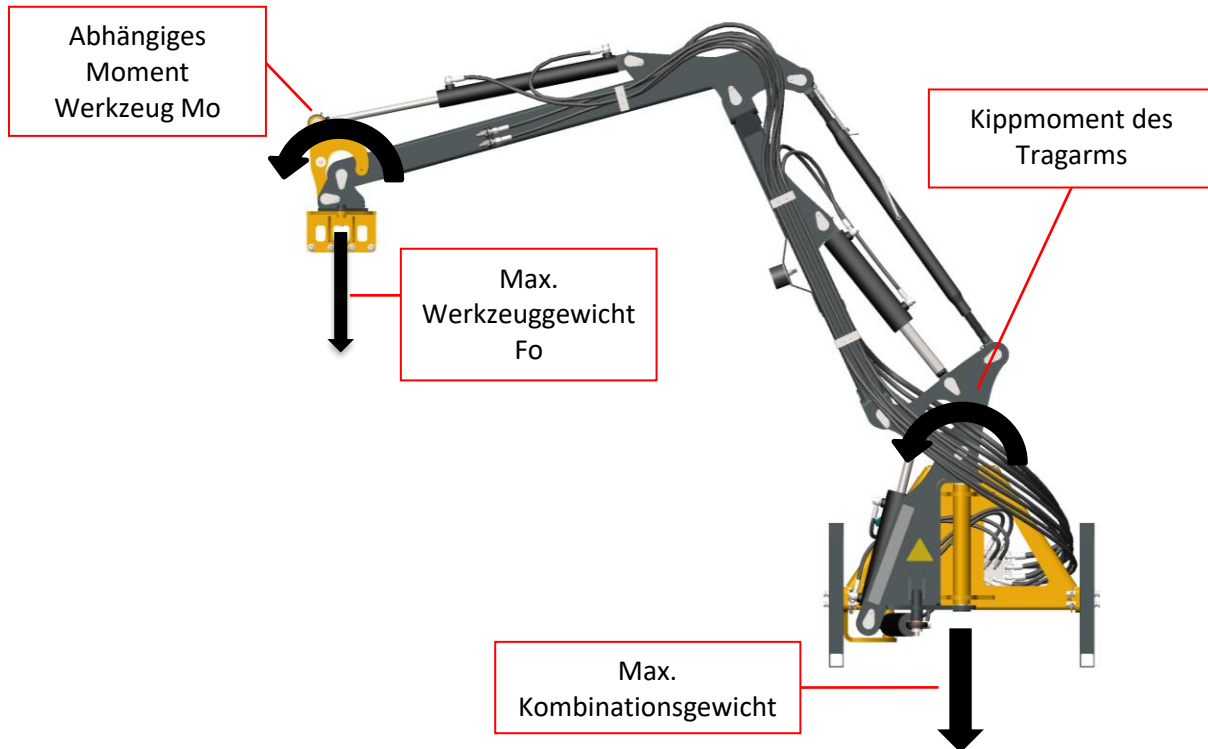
Maximale Belastung von Werkzeugträger und Werkzeug.
